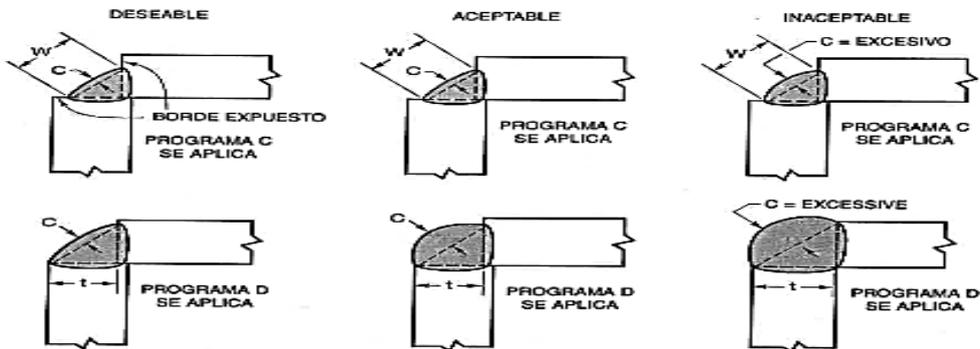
Perfiles de soldadura de filete juntas de esquina exterior-interior (ver tabla 4).
